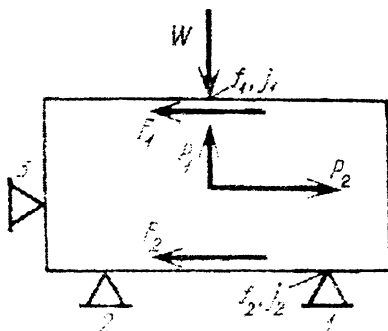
Схема установки заготовки и схема действующих на нее сил
